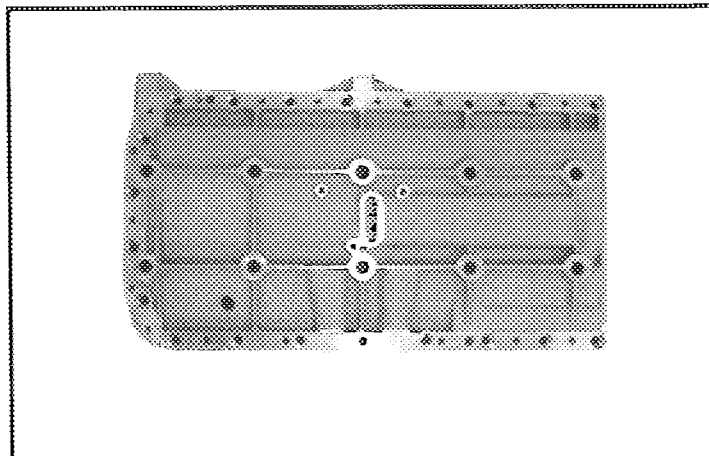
PHOTO SEMELLE RENFORT BLOC ET PALIERS
